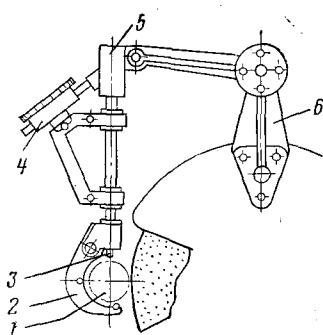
Приспособление для контроля размера шеек коленчатого вала в процессе их шлифования
